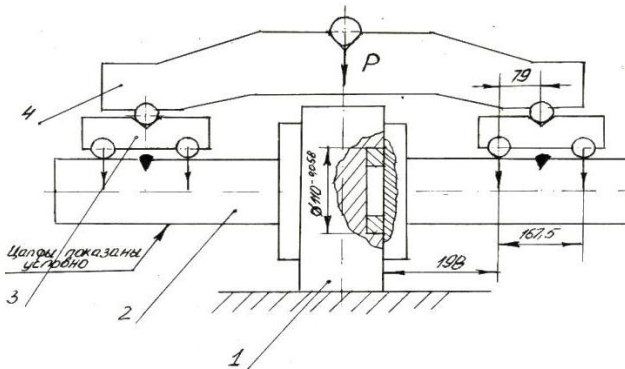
Схема приспособления для циклических испытаний цапф при изгибе:
